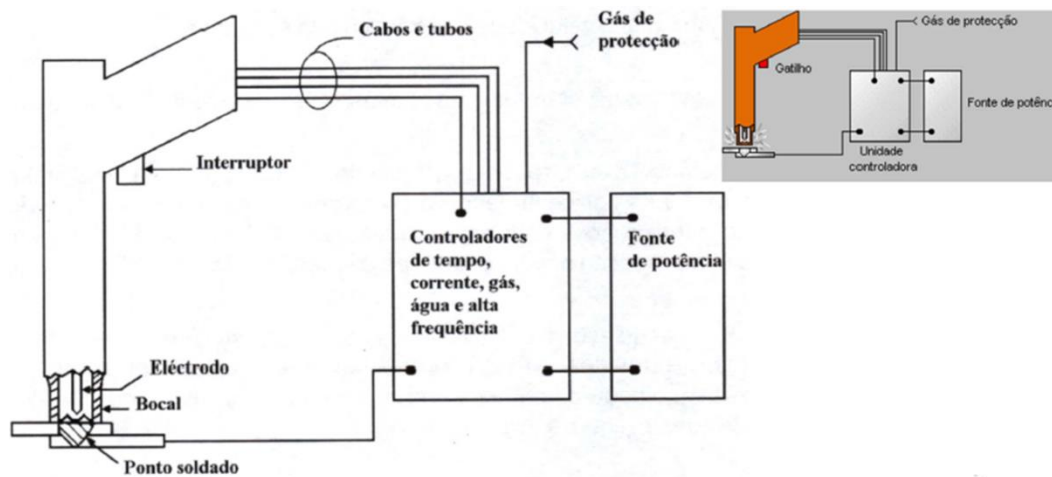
Representação esquemática de uma instalação de soldadura para o processo TIG (Por Pontos) [27].
